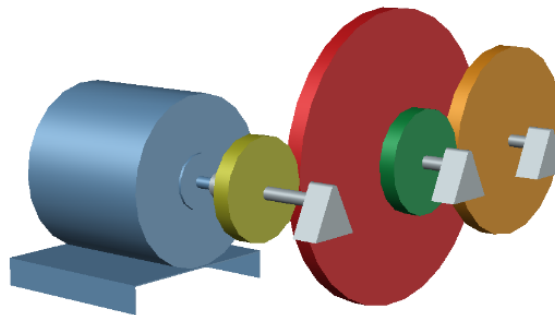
Disposición de rodamientos y apoyos para la caja reductora
